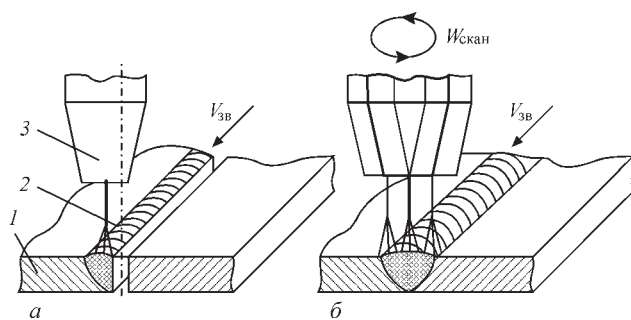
MAG зварювання тонколистового металу: а – зварювання без скануючих рухів пальника (дуга перекинулася на одну із крайок і плавить тільки її в зоні стику); б – зварювання зі скануючими рухами пальника поперек стику або по колу
